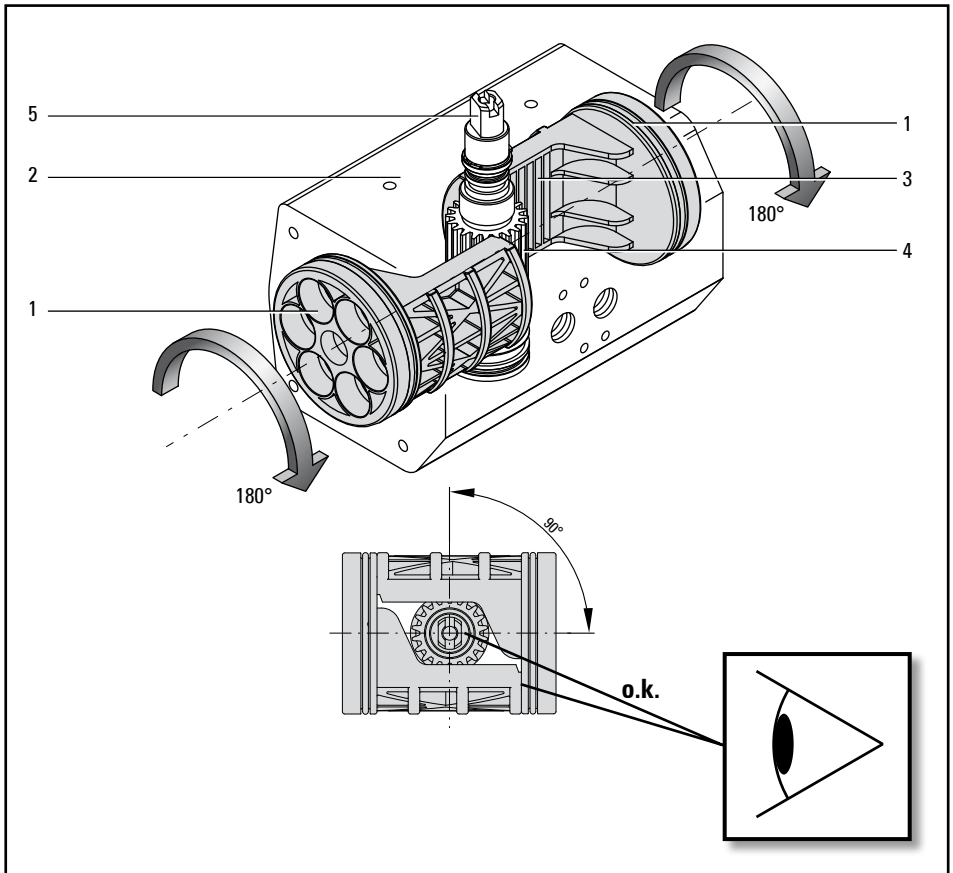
Drehrichtung ändern, Kolben drehen
